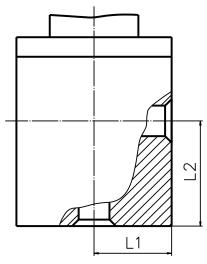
螺纹法兰或焊接连接的角式截止阀的结构长度示意图
